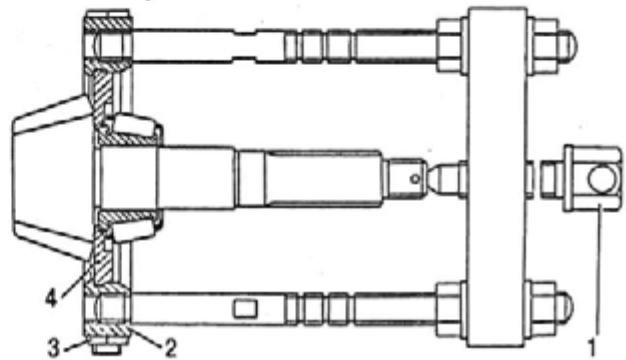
Снятие внутреннего кольца заднего подшипника с ведущей шестерни:
